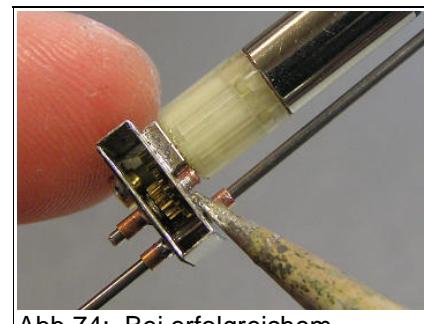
Bei erfolgreichem Testlauf kann die Buchse mit eingesteckter Welle am Getriebegehäuse angelötet werden.
